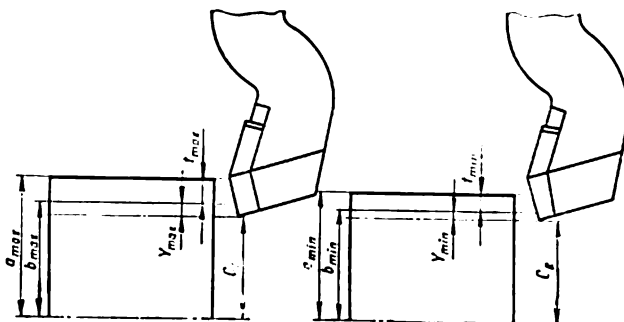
Illustration du calcul de la cote de position pour l'usinage des surfaces extérieures
